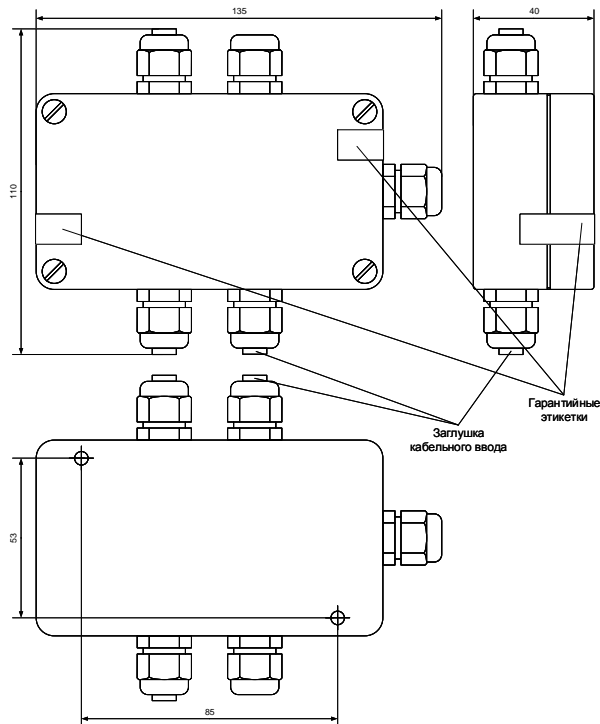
Внешний вид, габаритные и установочные размеры счетчика СИПУ xxx.xx.B5
